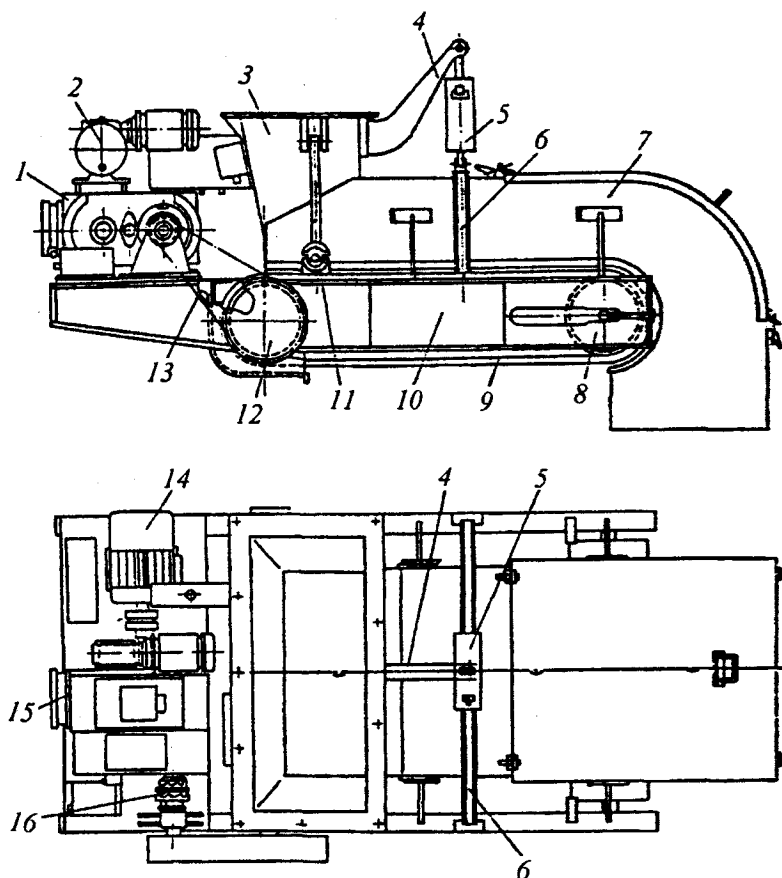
Конструкція вагового дозатора С-864 для заповнювачів:
